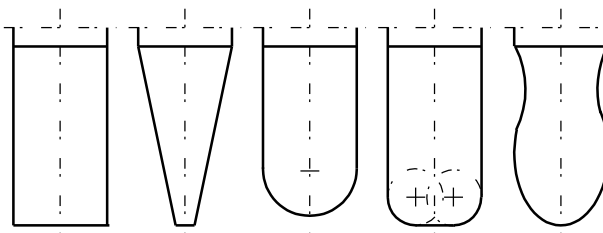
Исходные инструментальные поверхности инструментов для обработки сложных поверхностей деталей.
